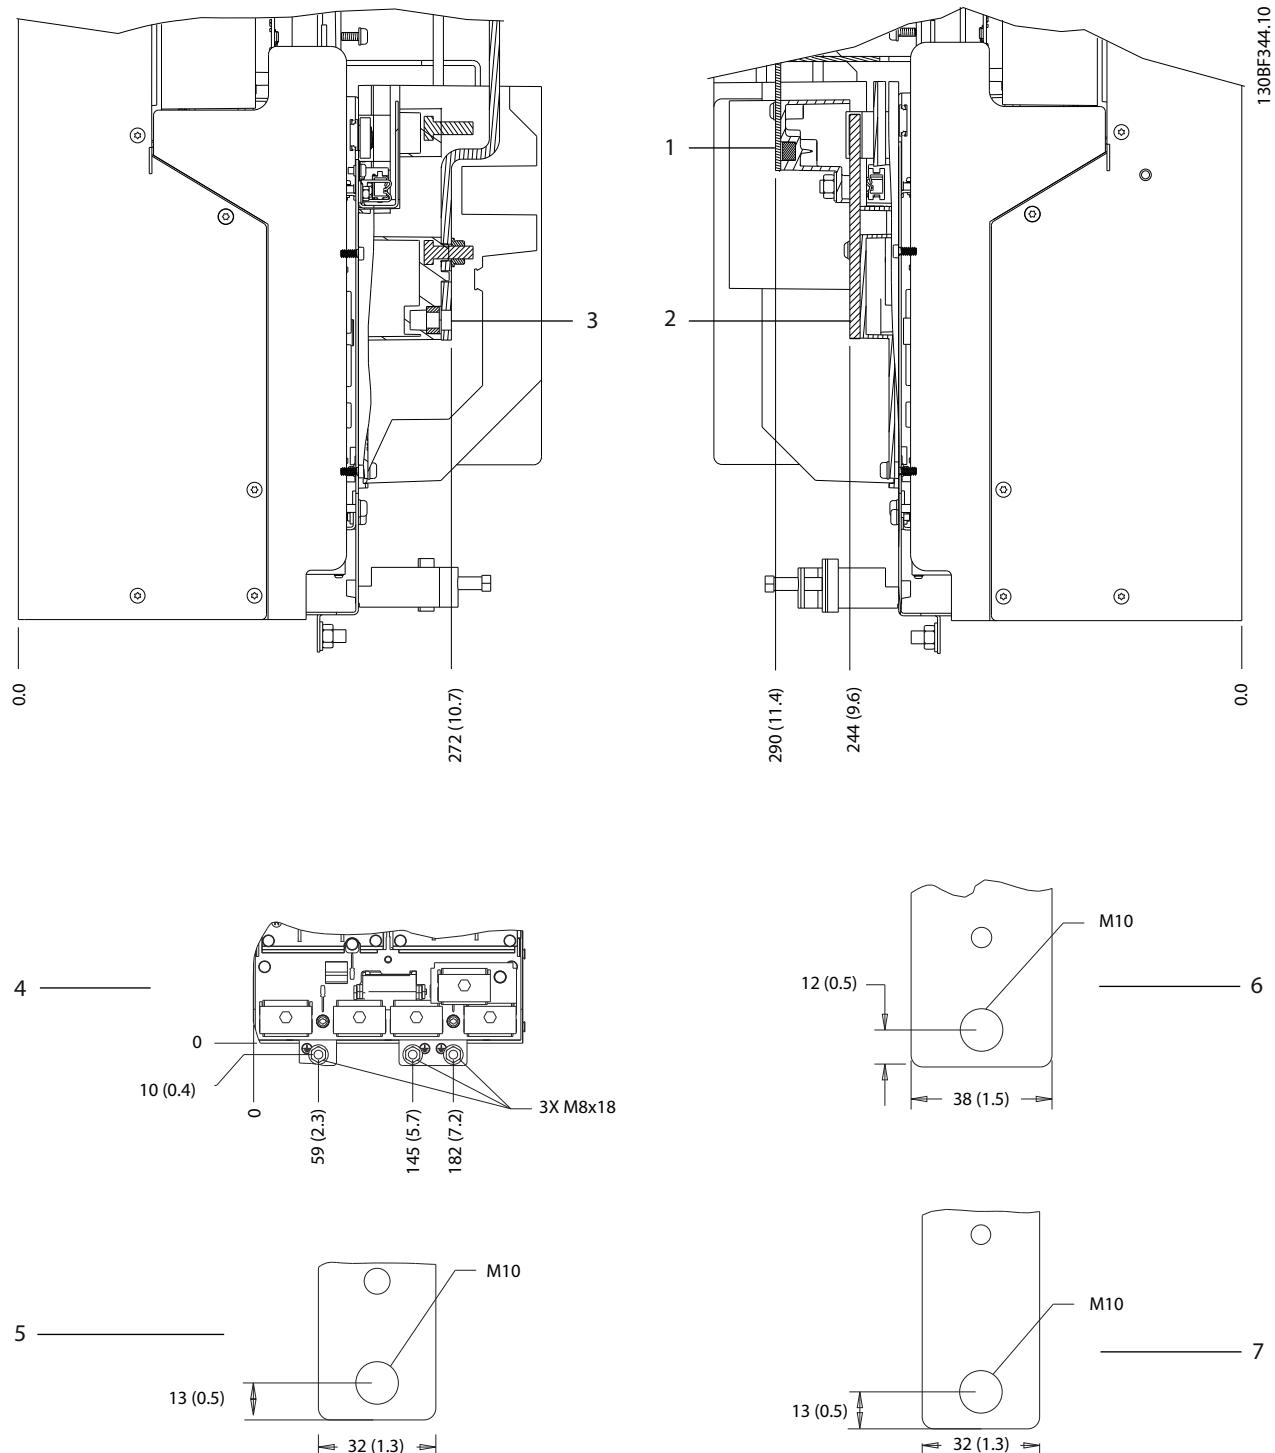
Dimensi Terminal D2h (Tampak Samping)
